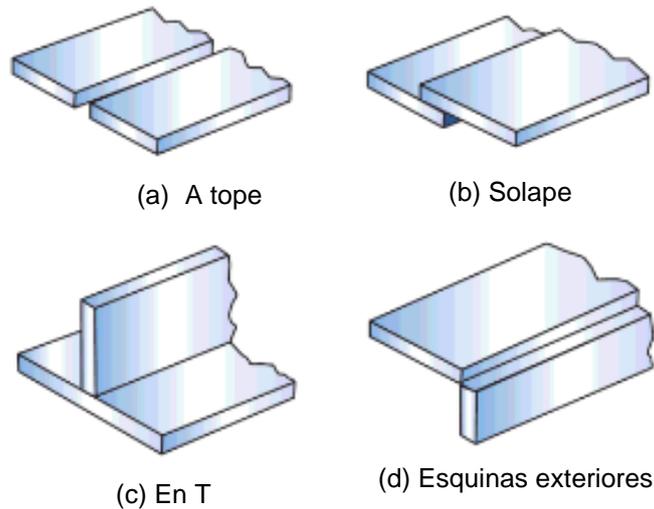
Diferentes tipos de juntas soldadas
